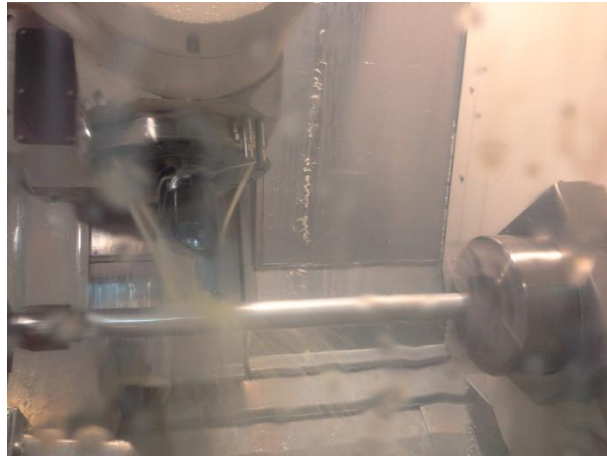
เครื่องจักร CNC Swiss Type Lathe
